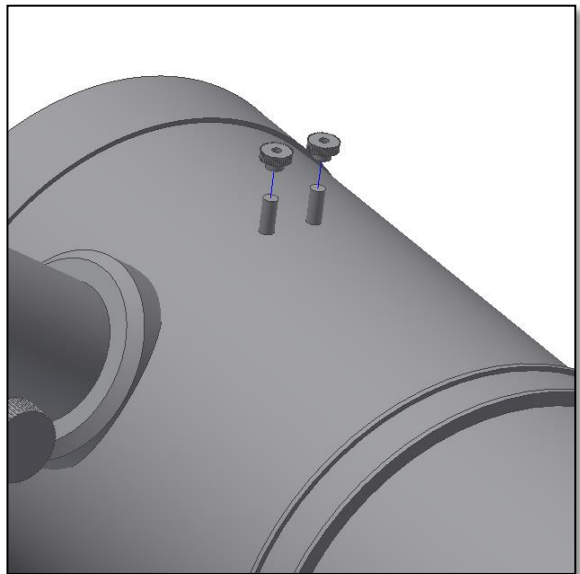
Rändelschrauben des Sucherfernrohrs entfernen.
